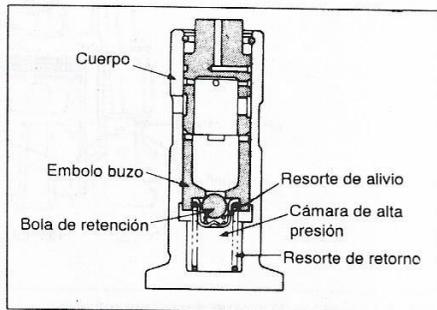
Estructura del levantaválvulas hidráulico.
